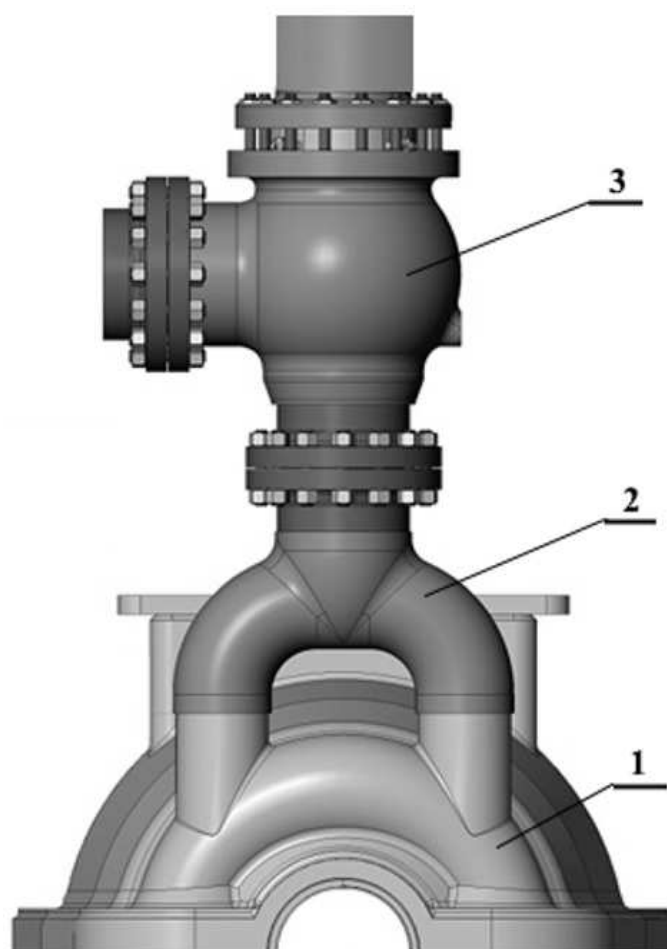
Эскиз установки регулирующего клапана на верхнюю половину корпуса ЦВД:
